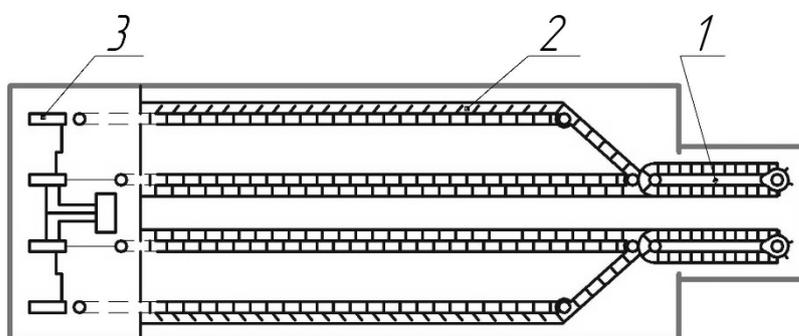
Схема транспортера навозоуборочного возвратно – поступательного движения (штангового) УН-3,0.
